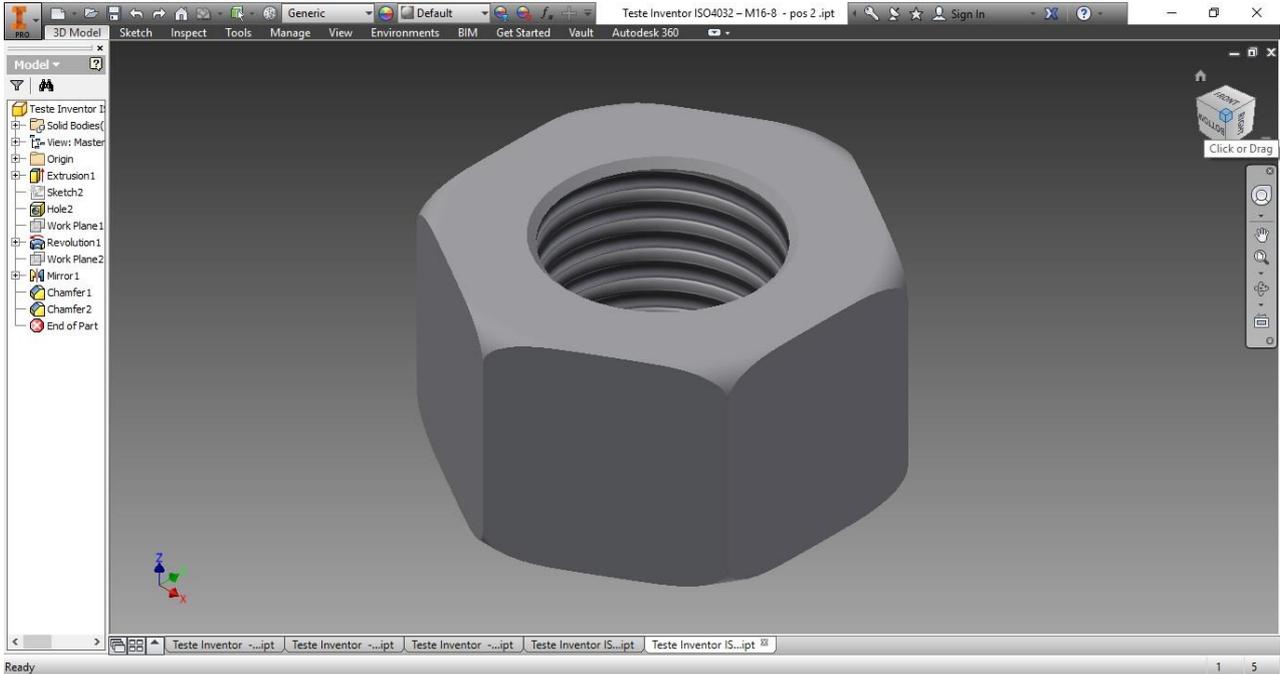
Posição nº 2 – Porca ISSO 4032 – M16-8
